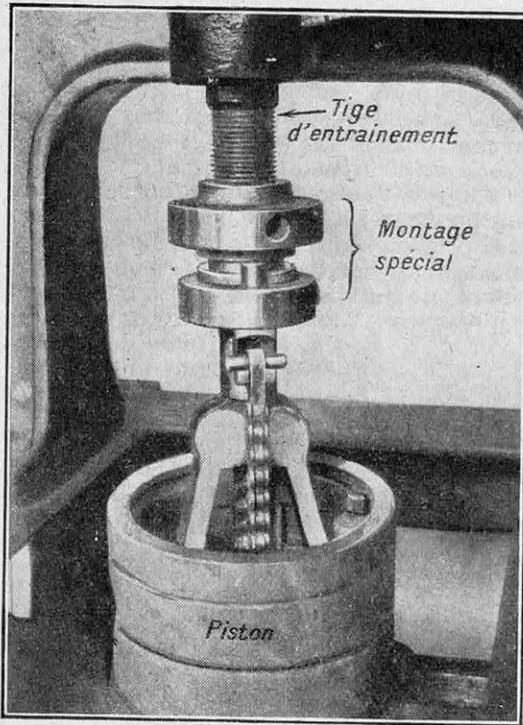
MONTAGE D'UN PISTON POUR RODAGE DES SEGMENTS (MIS A LA PLACE DU RODOIR) SUR LA MACHINE GUNTHER
